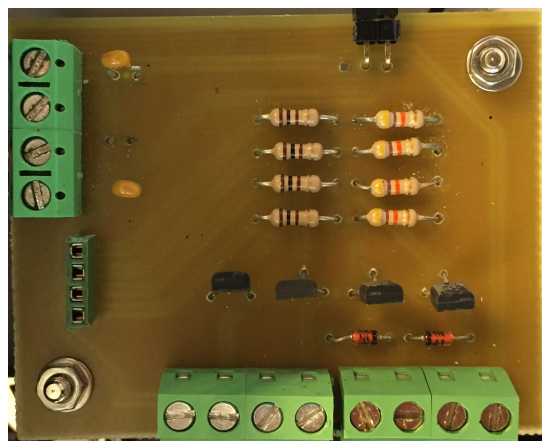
PCB terminada con componentes soldados en estaño
